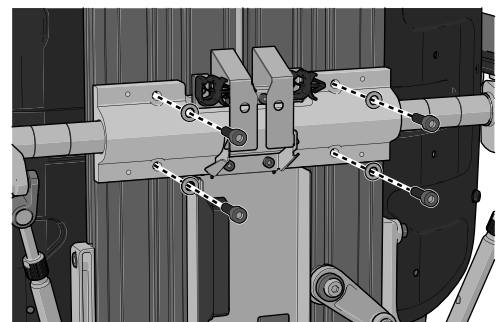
Die Armlehnen sind mit vier Schrauben befestigt.
